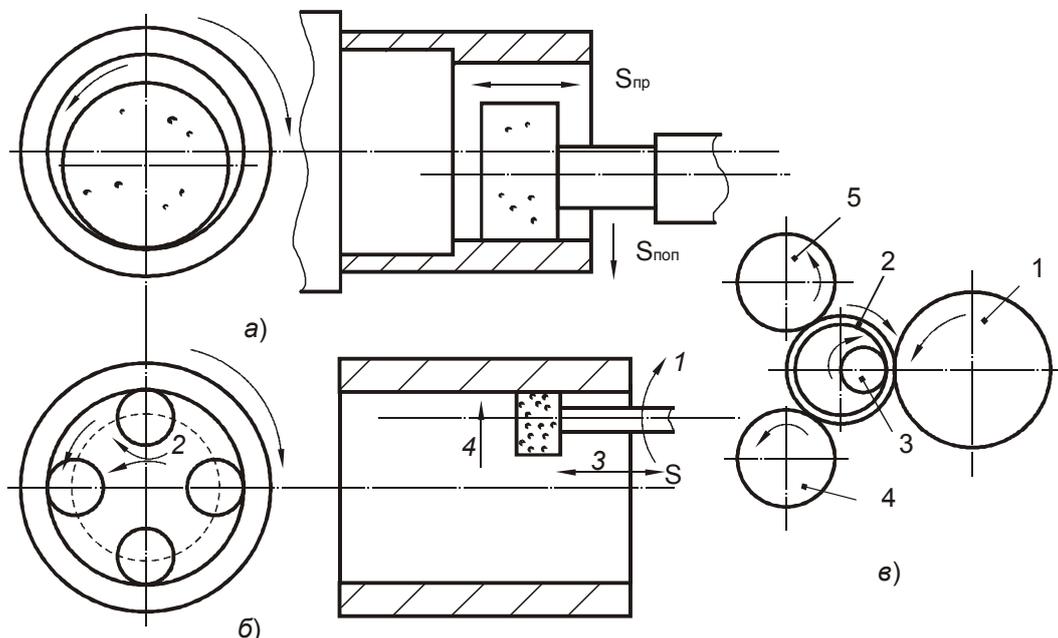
Виды внутреннего шлифования: а – во вращающейся заготовке; б – планетарное; в – бесцентровое
